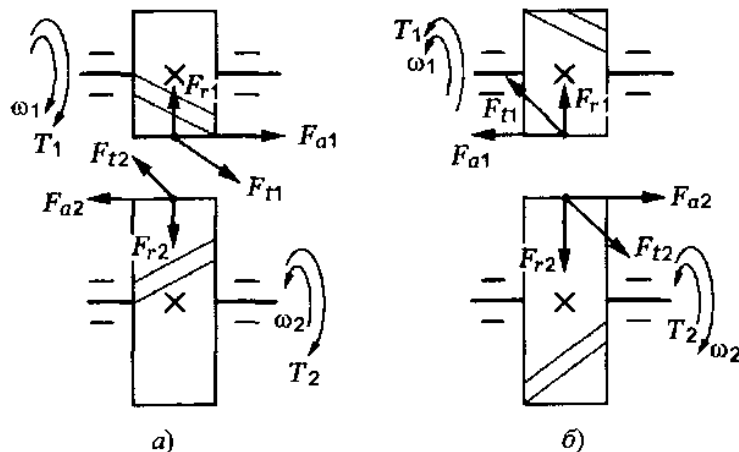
Схемы сил в зацеплении косозубой цилиндрической передачи:
